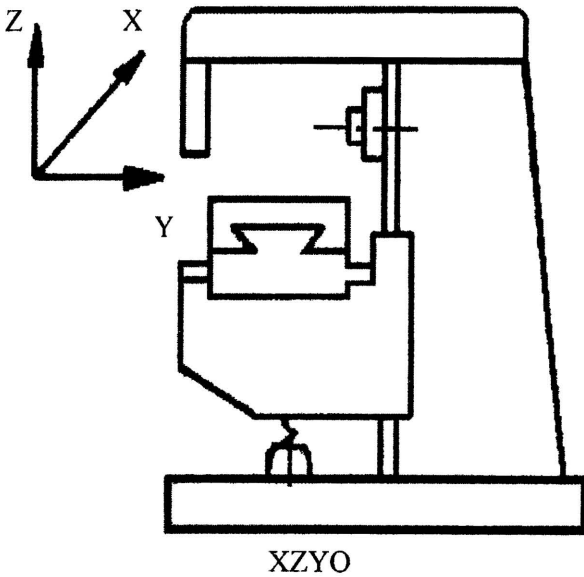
Компонівка горизонтально-фрезерного станка
